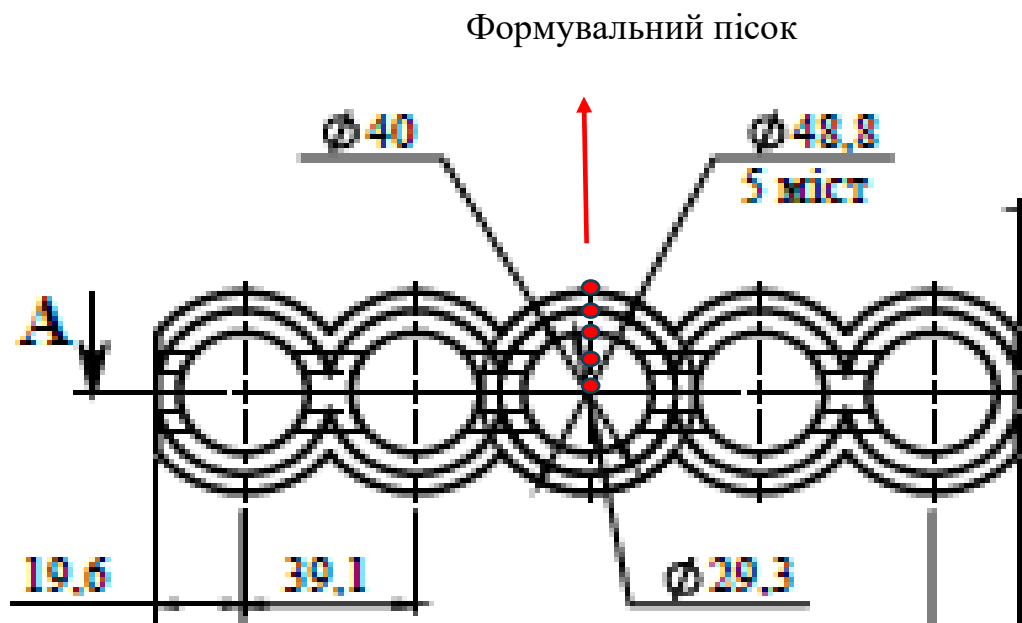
Схема розрахункової області (центрального перерізу виливка) з позначенням контрольних точок: 1 - центр наповнювача; 2 -  $\frac{1}{2}$  радіуса неметалевої фази (наповнювача); 3 - межа розділу фаз «метал–наповнювач»; 4 - середина стінки виливка ( $\frac{1}{2}$  товщини); 5 - зовнішня поверхня виливка (межа з сухим формувальним піском).
